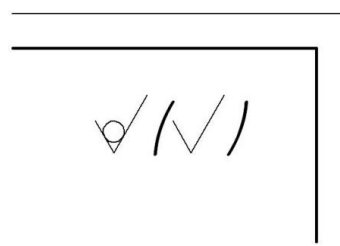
Обозначение шероховатости в правом верхнем углу чертежа (вариант 2)
